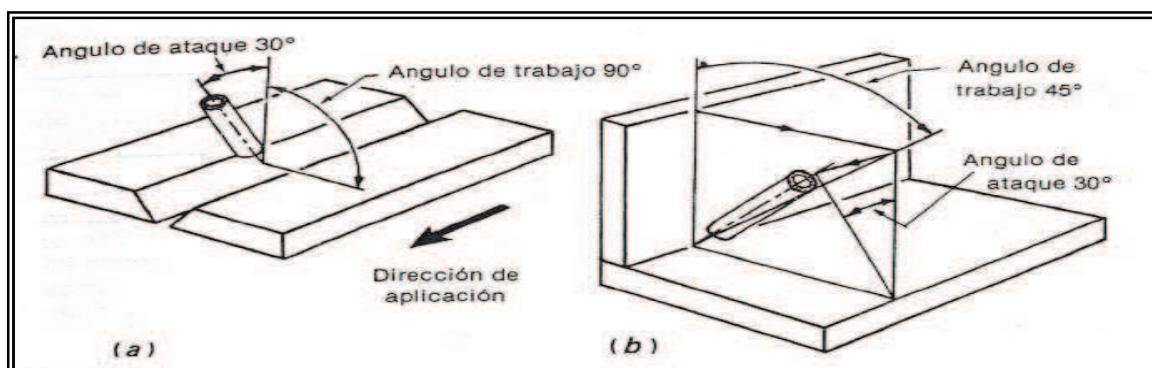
Posición del electrodo para soldadura de arco.
